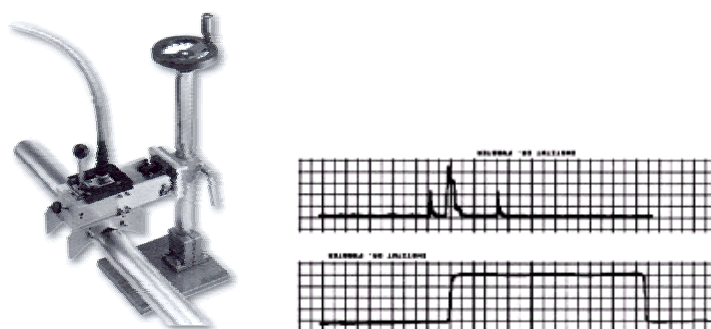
Контроль продольно-сварной стальной трубы на наличие коротких дефектов поверхности и разрывов (открытый сварной шов)
